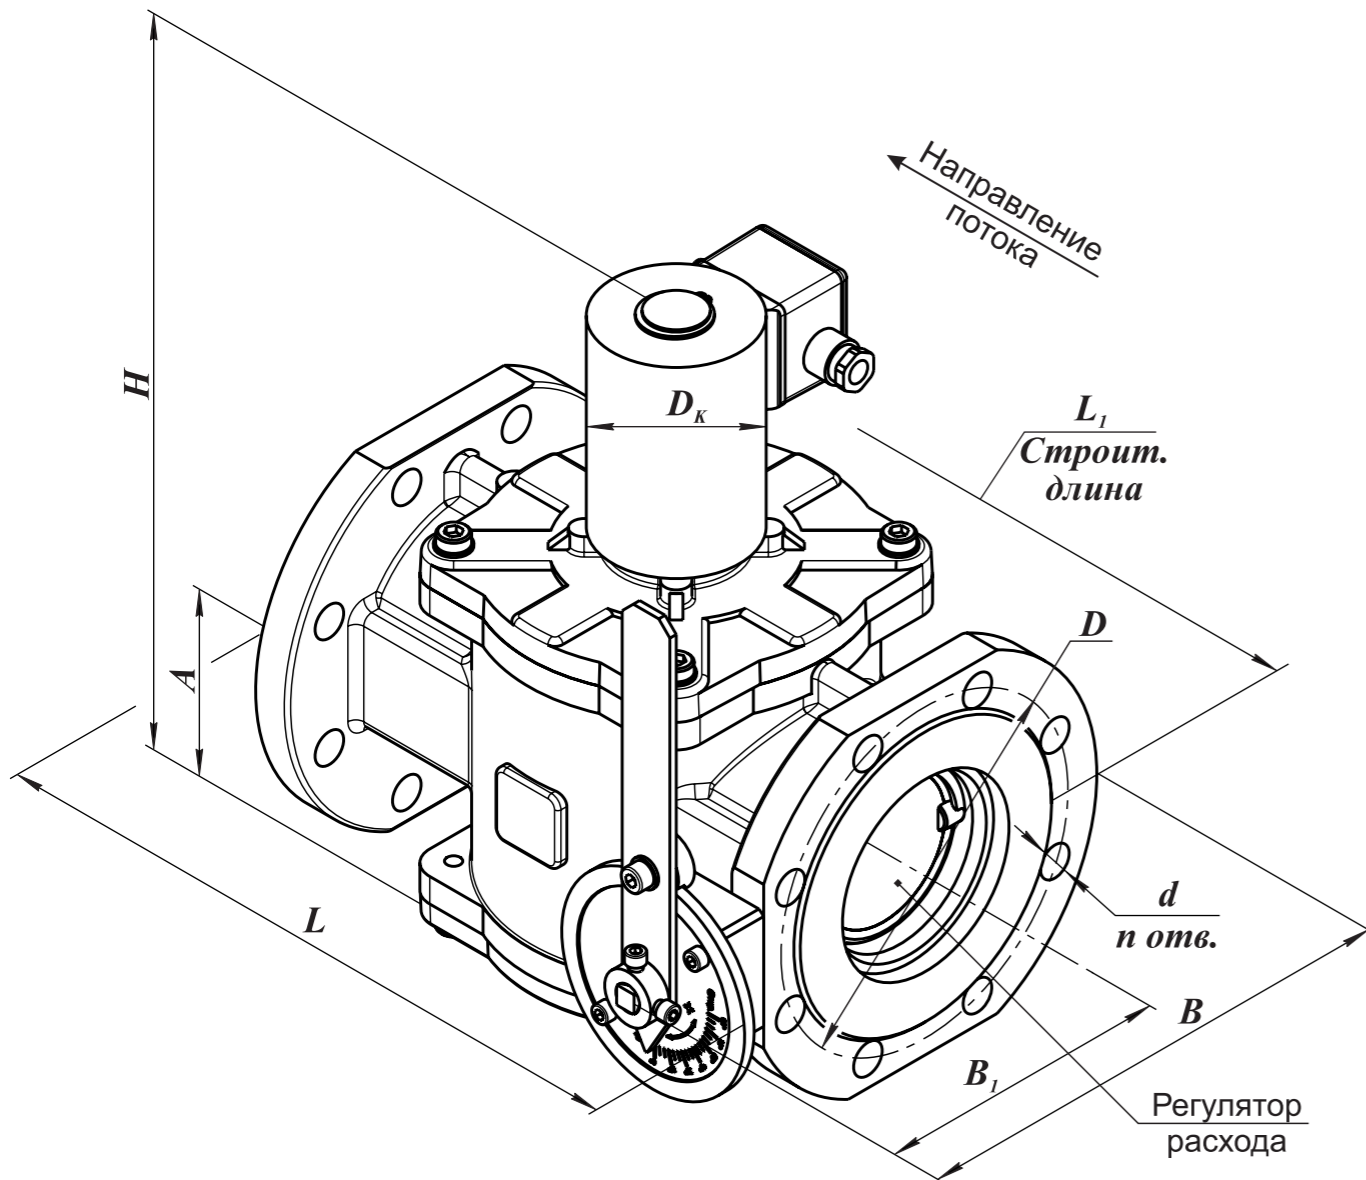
Клапаны на DN 65 - 100 фланцевые с ручным регулятором расхода (исполнение: с присоединительными фланцами PN 16)
